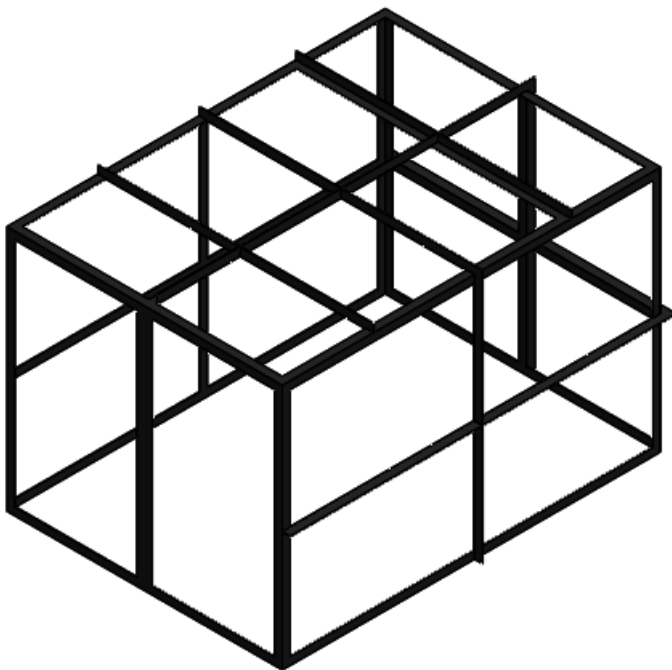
Vista Isométrica de la estructura metálica exterior del horno
